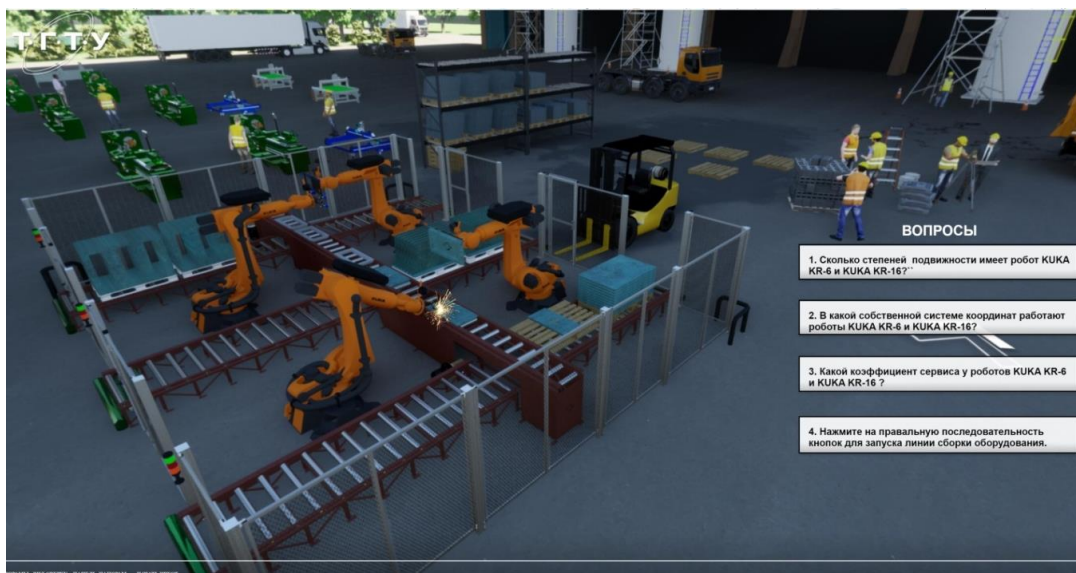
Визуализация производственного участка, включающего роботизированный сварочный комплекс фирмы KUKA
